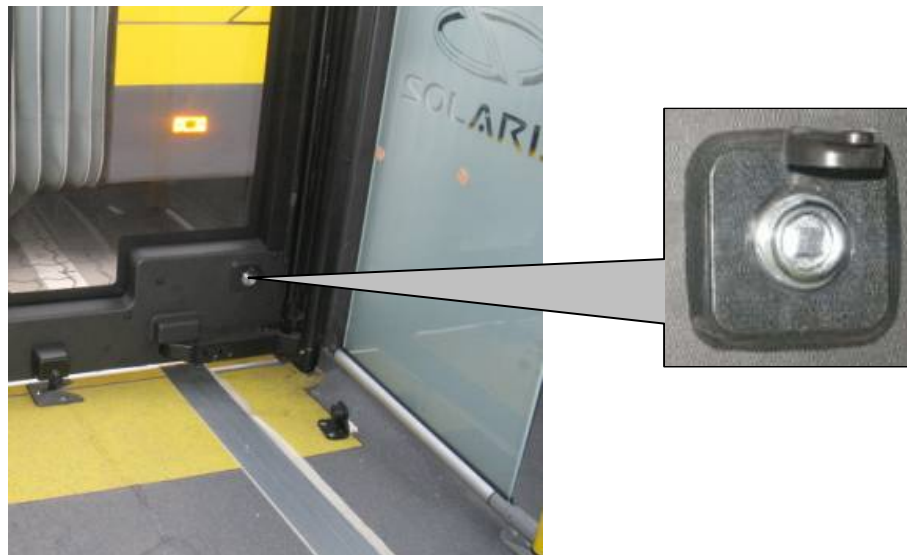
Zamek patentowy pierwszego skrzydła przednich drzwi – wskazany strzałką
